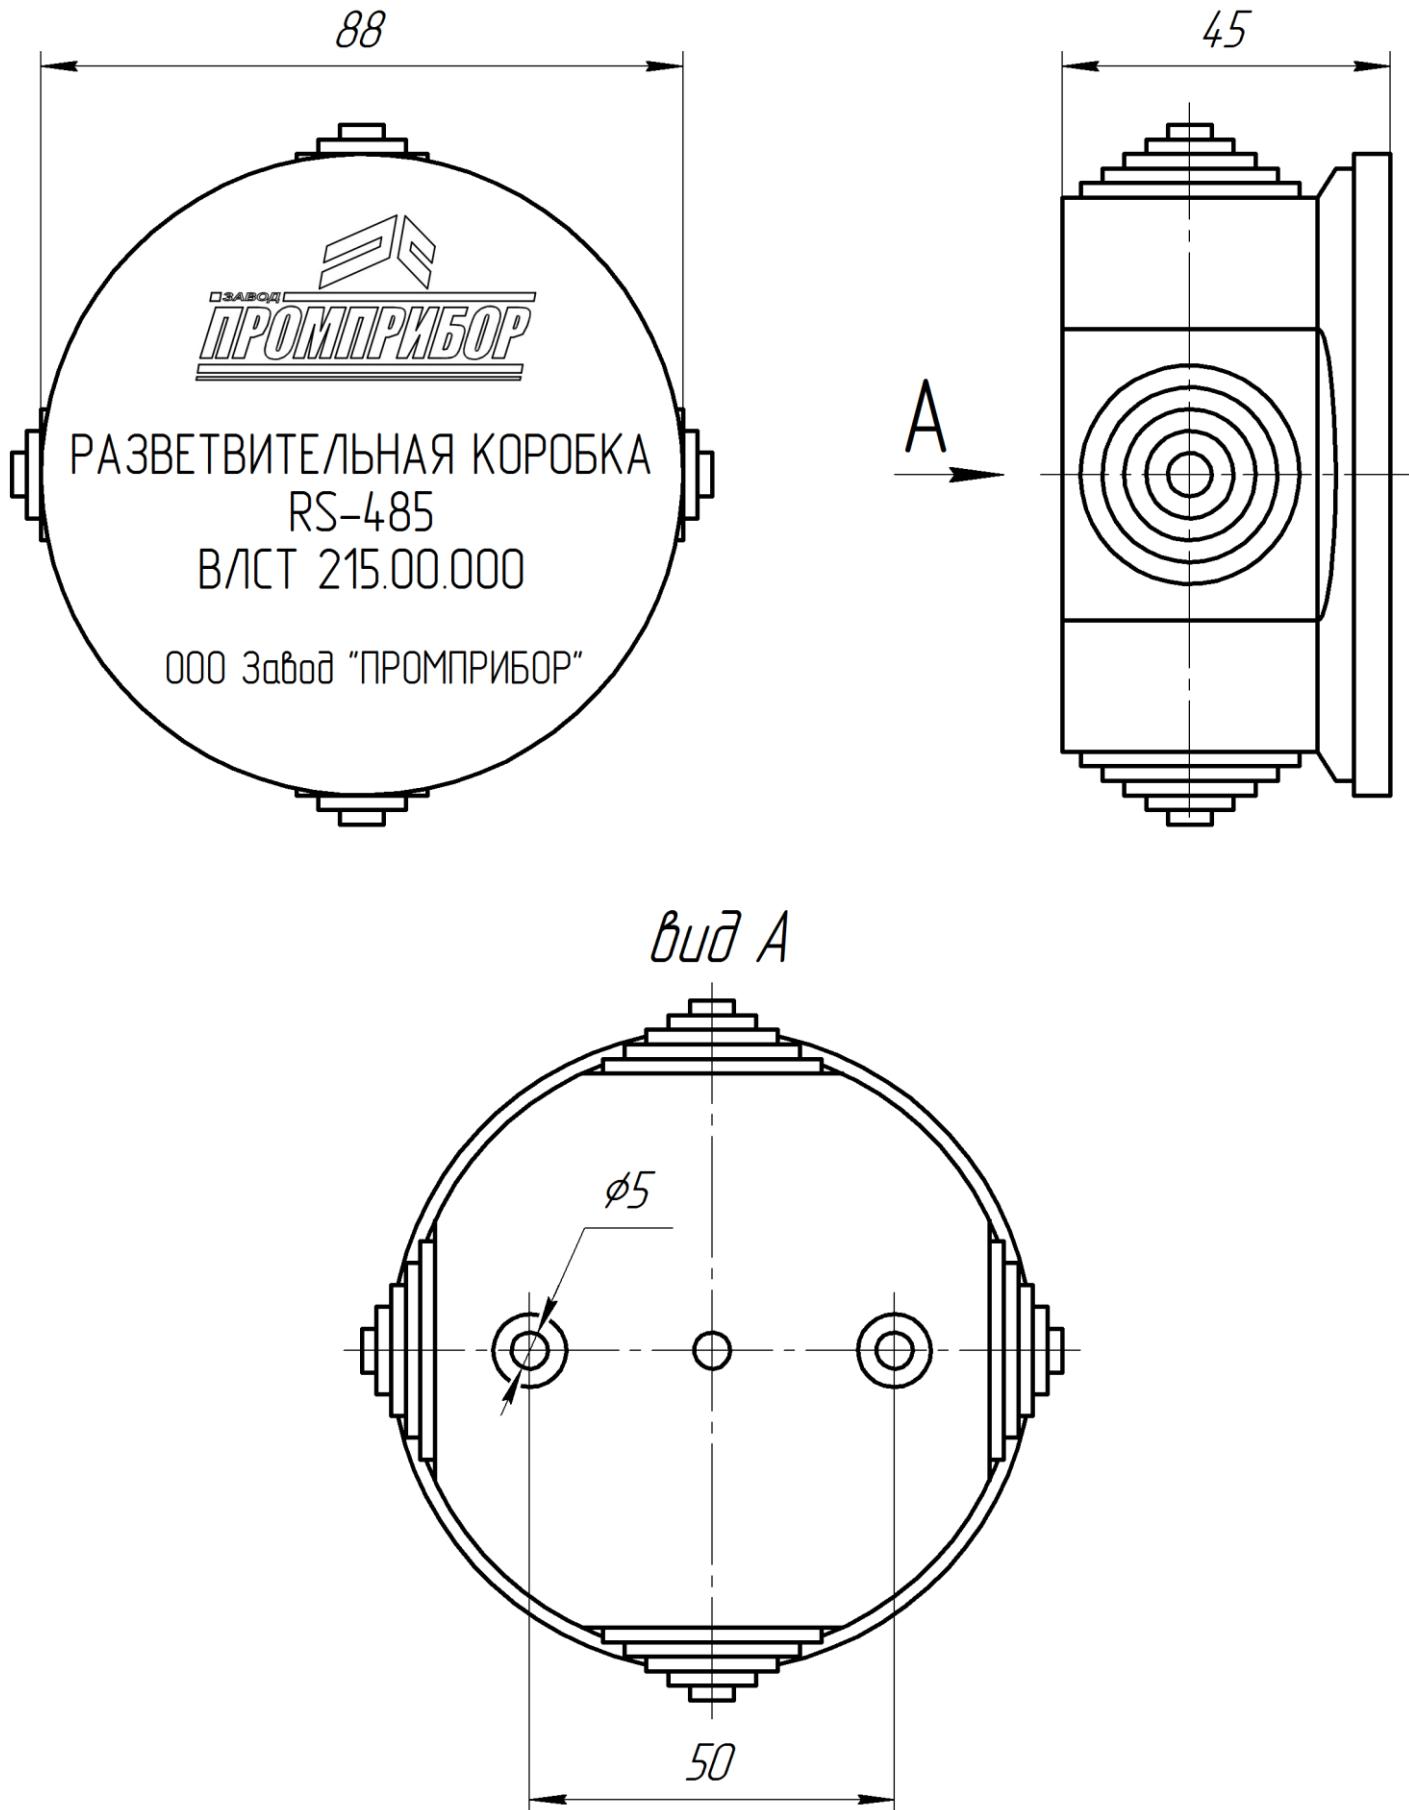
Габаритные и присоединительные размеры разветвительной коробки
